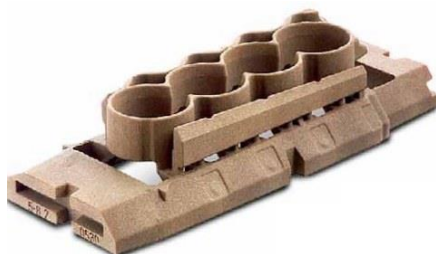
Песчаные стержни блока цилиндров двигателей
